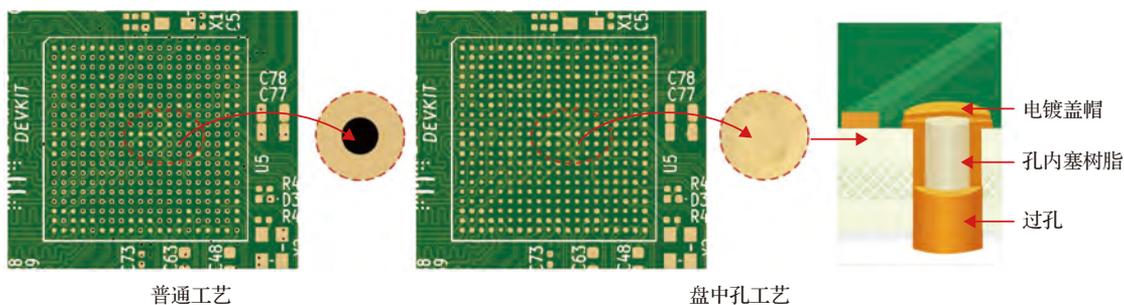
普通工艺与盘中孔工艺生产的 BGA 焊盘
